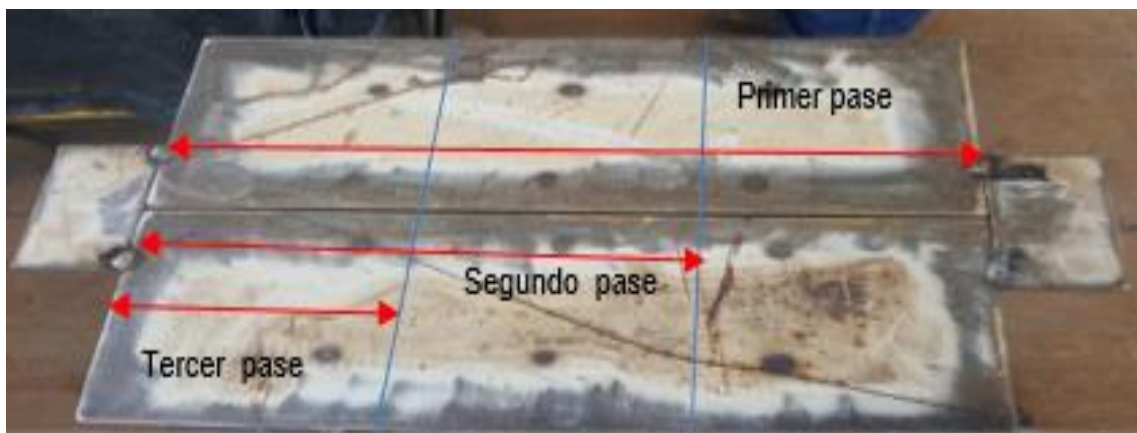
División de probetas, aplicación de cordones de soldadura
